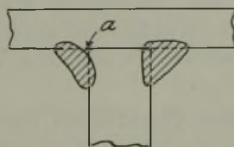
Schweißverbindung mit Schlackeneinschluß durch abgerundete Kante (a).
